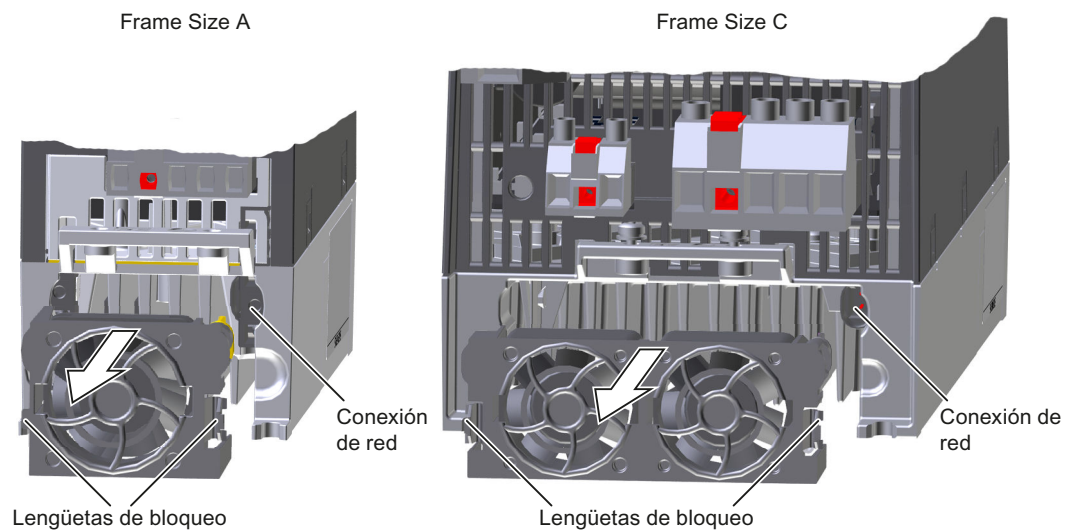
Desmontaje de la unidad de ventilador del disipador
